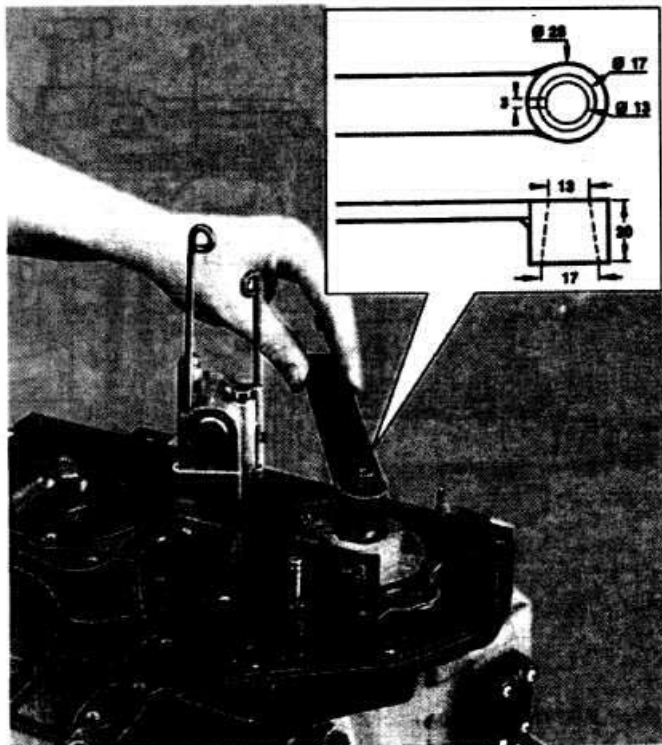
Установка вала привода ТНВД с помощью приспособления BMW 13.5.062
